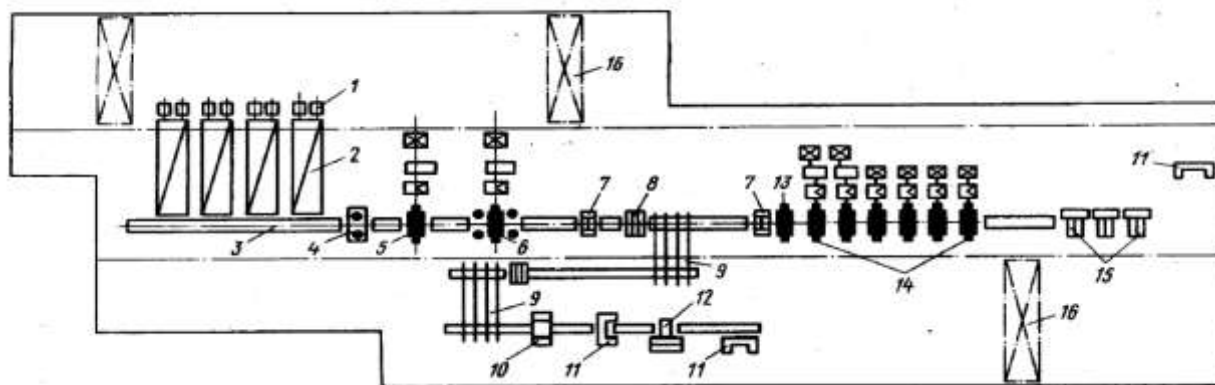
Схема основного технологического оборудования стана 2300/1700: 1 – толкатели, 2 – нагревательные печи, 3 – рольганг, 4 – черновой вертикальный окалиноломатель, 5 – уширительная клетка 2300, 6 – универсальная клетка 2300, 7 – ножницы, 8 – роликотправильная машина, 9 – шлепперы, 10 – дисковые ножницы, 11 – ножницы гильотинные, 12 – маркировочная машина, 13 – чистовой окалиноломатель, 14 – рабочие клетки чистовой группы, 15 – моталки, 16 – краны
